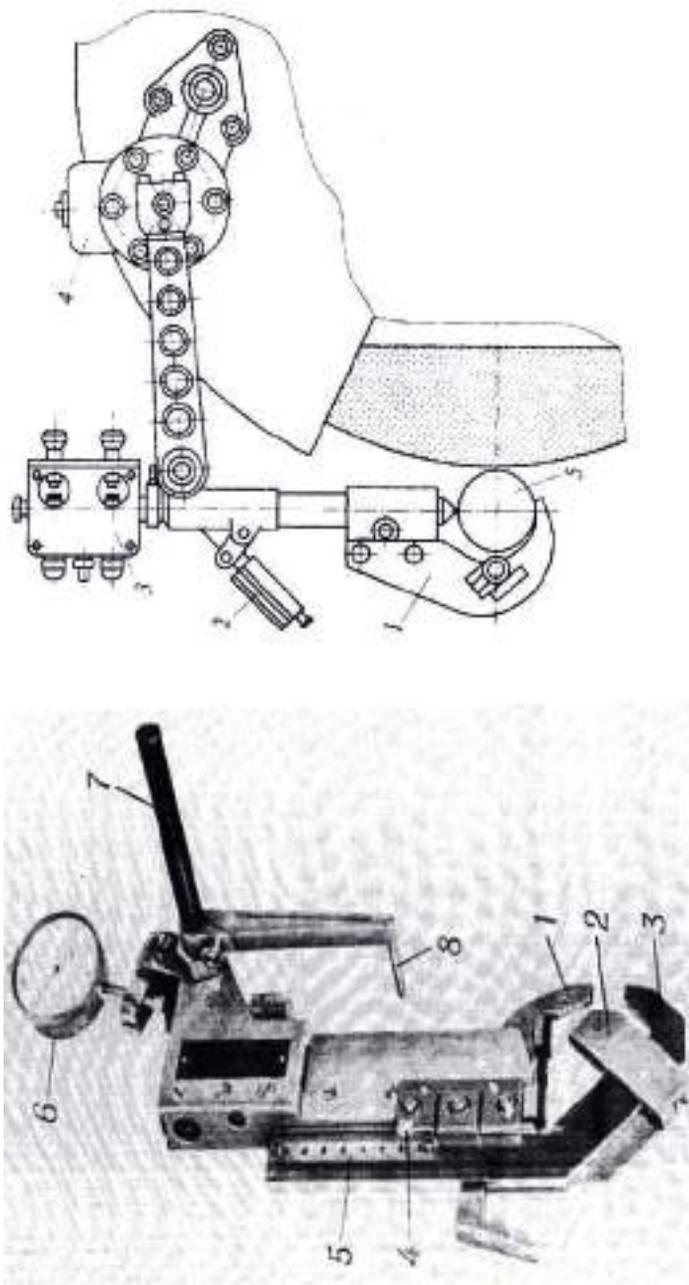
Схема автоматического контроля вала устройством автоматического контроля с трёхконтактной скобой: 1, 3 – регулируемые контакты; 2 – контролируемая заготовка; 4 – указатель; 5 – шкала для предварительной настройки на размер; 6 – индикатор; 7 – кронштейн; 8 – ограничитель
